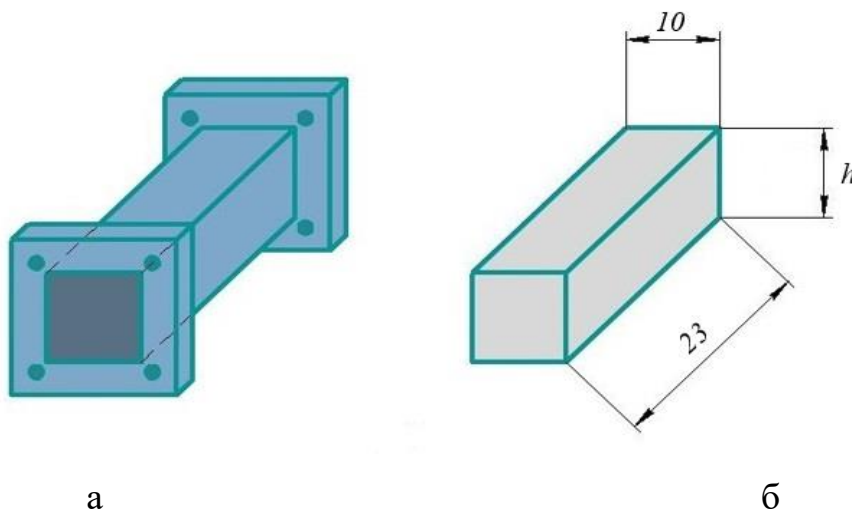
Внешний вид волновода и контрольного образца:
